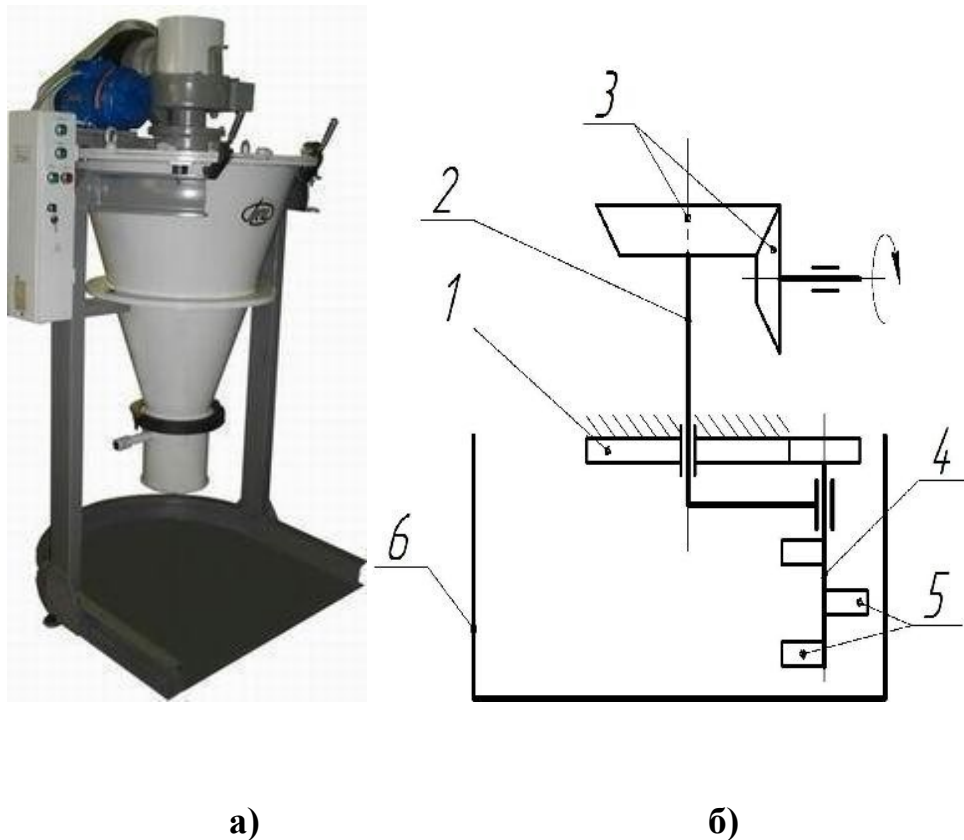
Загальний вигляд (а) та кінематична схема (б) планетарно-шнекового змішувача СПШ/20: 1 – змішувальний бункер; 2 – шнек; 3 – водило; 4 – шестерні; 5 – нерухома закріплена шестерня.
